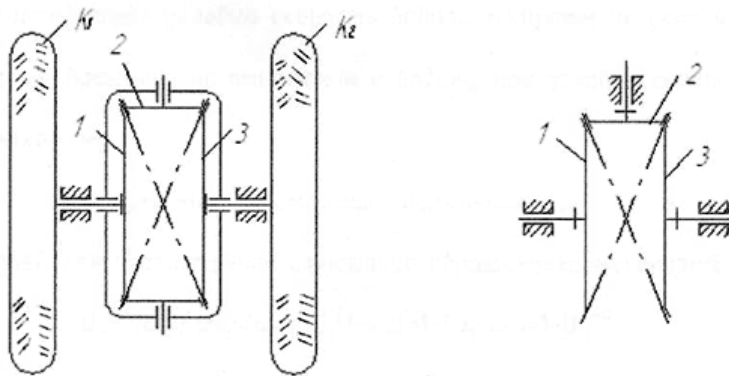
Дифференциальный механизм с коническими зубчатыми колесами
